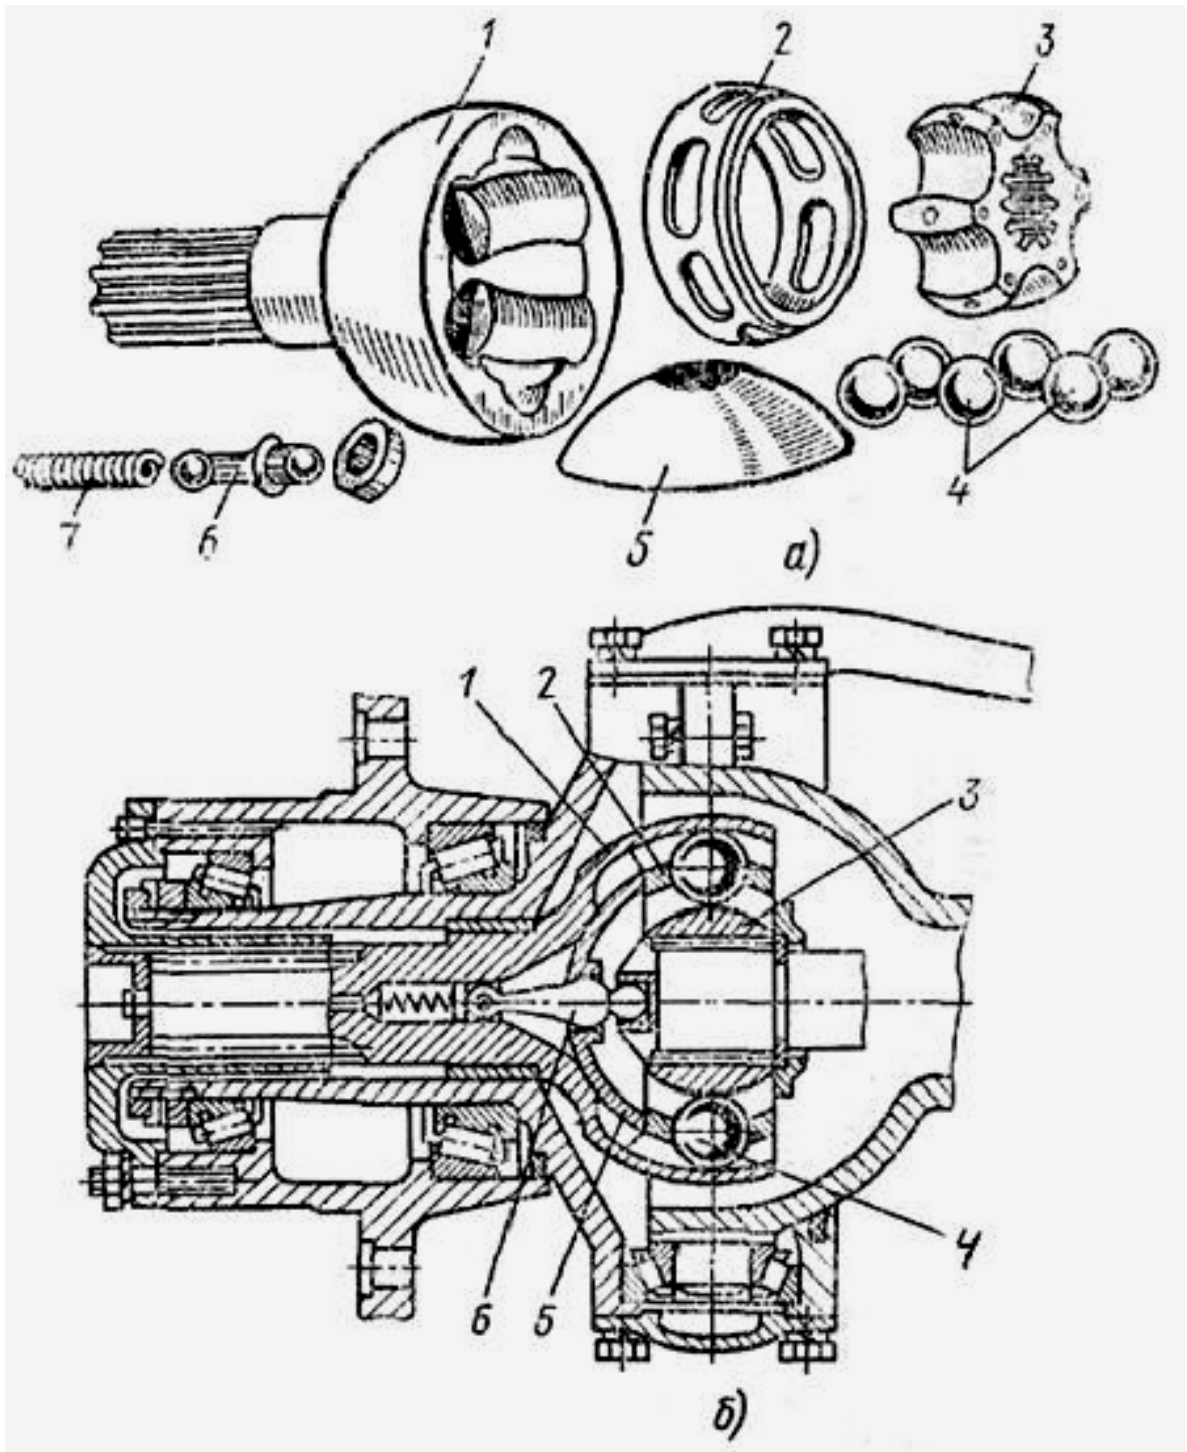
Карданная передача с шарнирным карданным шарниром равных угловых скоростей с делительным рычажком: а – детали шарнира; б – продольный разрез. 1 - чашка; 2 - сепаратор; 3 - обойма; 4 - шарики; 5 - сферическая чашка; 6 - делительный рычажок; 7 - пружина
